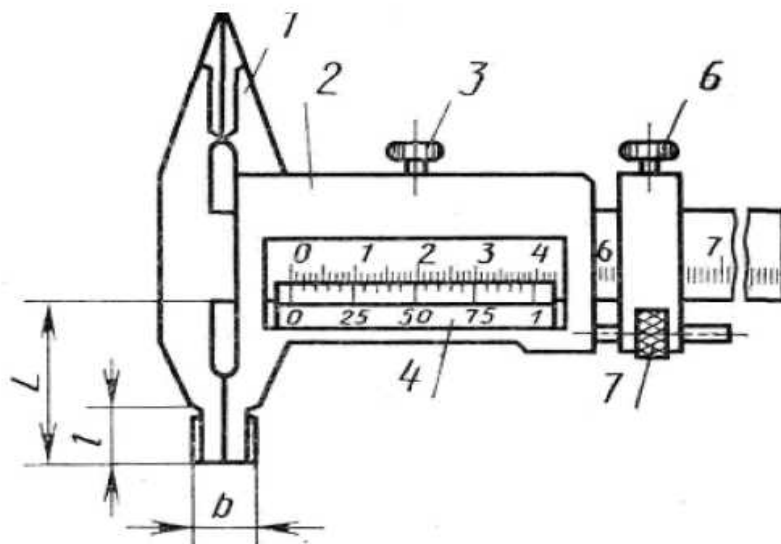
Общий вид штангенциркуля: 1 – измерительные губки; 2 – подвижная рамка; 3 – стопорный винт на подвижной рамке; 4 – нониус; 5 – винт на штанге; 6 – стопорный винт микрометрической подачи; 7 – микрометрическая подача для медленного перемещения рамки по штанге
